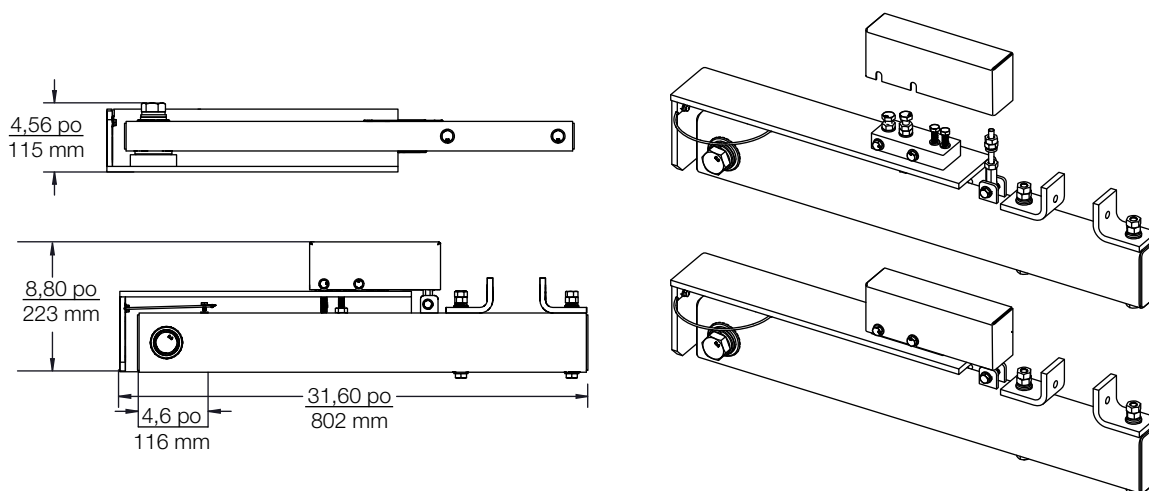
Vue du 221DB - Dimensions et assemblage
